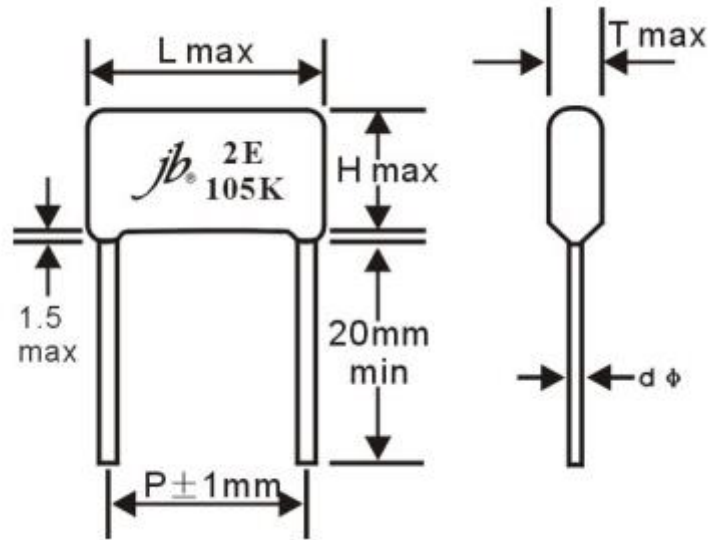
Габаритні розміри плівкового конденсатора
